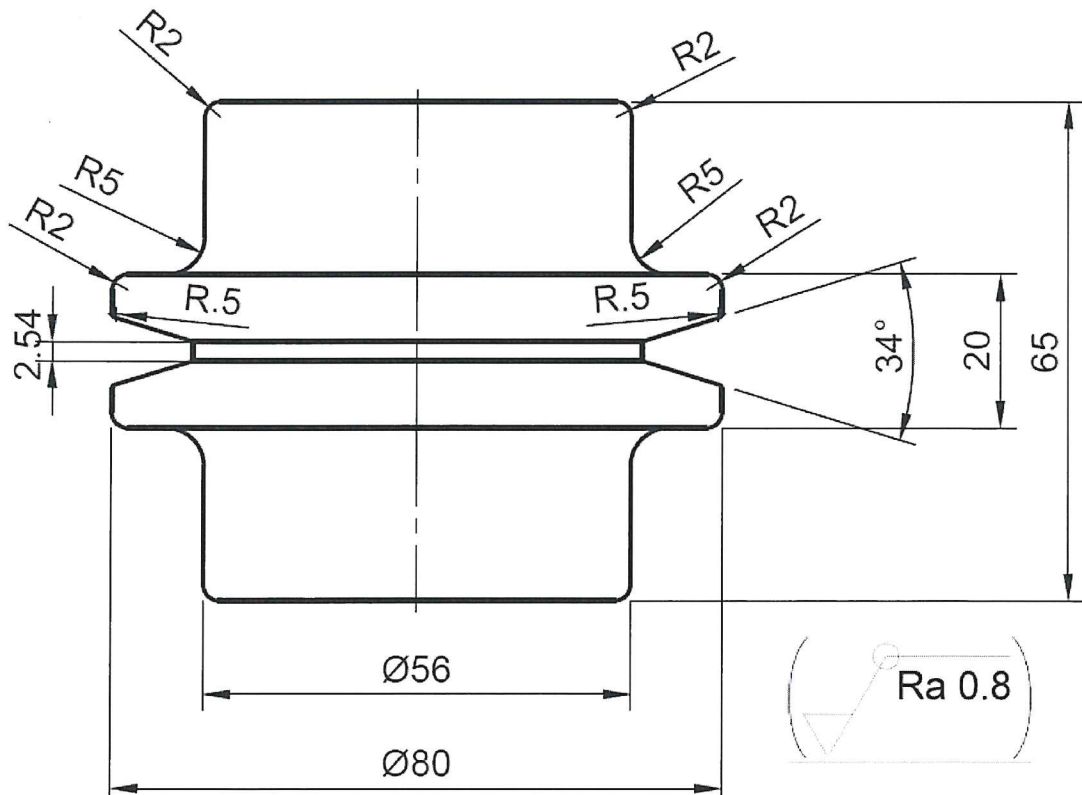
Disegno tecnico della puleggia oggetto di studio. Tutte le dimensioni sono espresse in millimetri.
